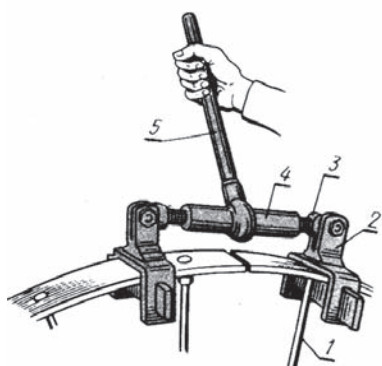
Приспособление для стягивания разорванного обода колеса: 1 – клин; 2 – кронштейн; 3 – винт; 4 – муфта; 5 – рукоятка.
